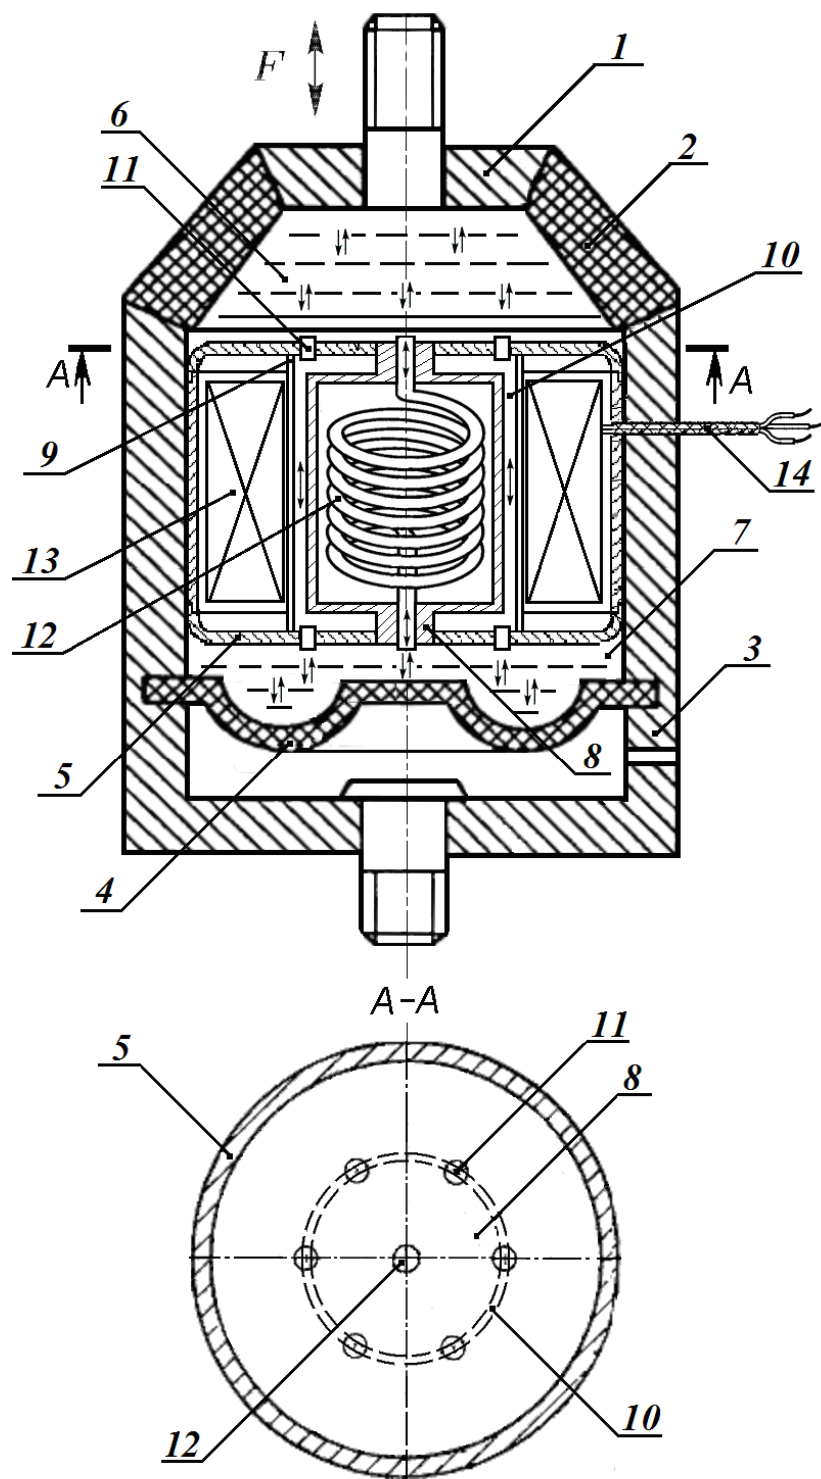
Структурная схема гидропоры с МРТ: 1 – опорная плата; 2 – обечайка; 3 – корпус опоры; 4 – мембрана; 5 – корпус дроссельной перегородки; 6, 7 – рабочая и компенсационная камеры; 8 – внутренний неподвижный цилиндр; 9 – внешняя цилиндрическая втулка; 10 – коаксиальный цилиндрический зазор с МРЖ; 11 – входные и выходные отверстия дроссельной перегородки; 12 – спиральный винтовой дроссельный канал; 13 – внешний однофазный индуктор; 14 – кабель питания внешнего индуктора гидропоры.
